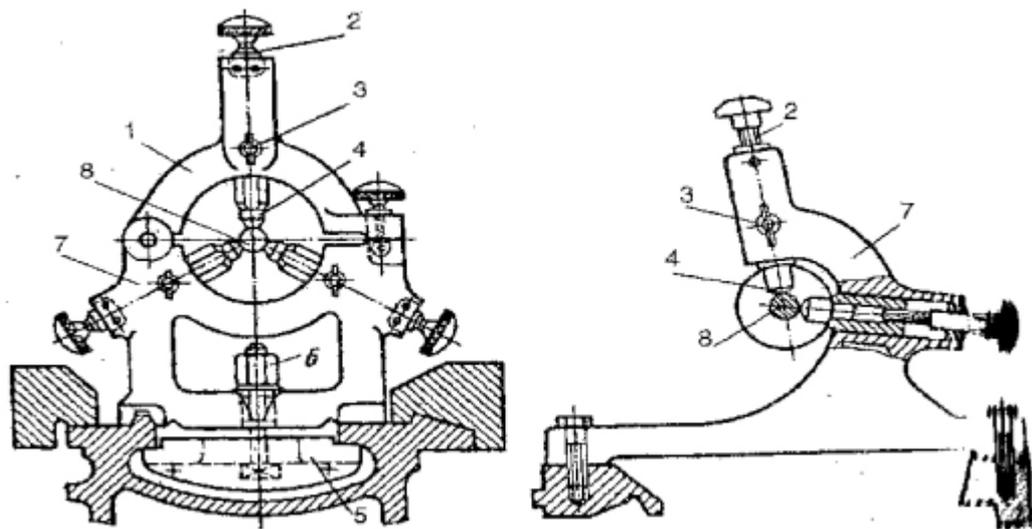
Конструкции люнетов: а – неподвижного; б – подвижного;
